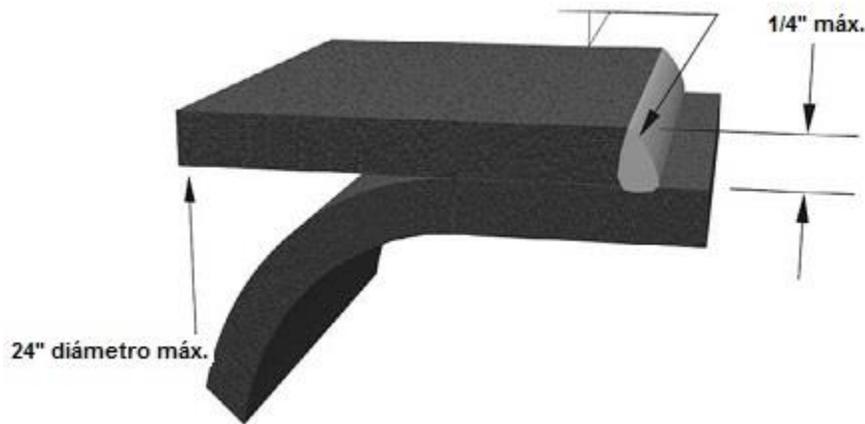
Unión por soldadura opción alterna cascarón-tapa de tipo 6.
